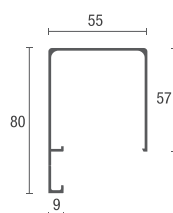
DETAIL ZÁKLADNÝ (SPODNÍHO PROFILU)
